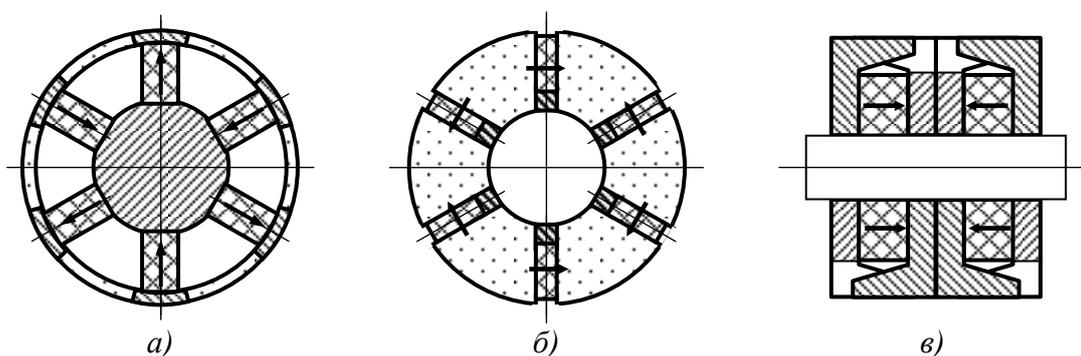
Схемы конструкции магнитоэлектрического ротора
